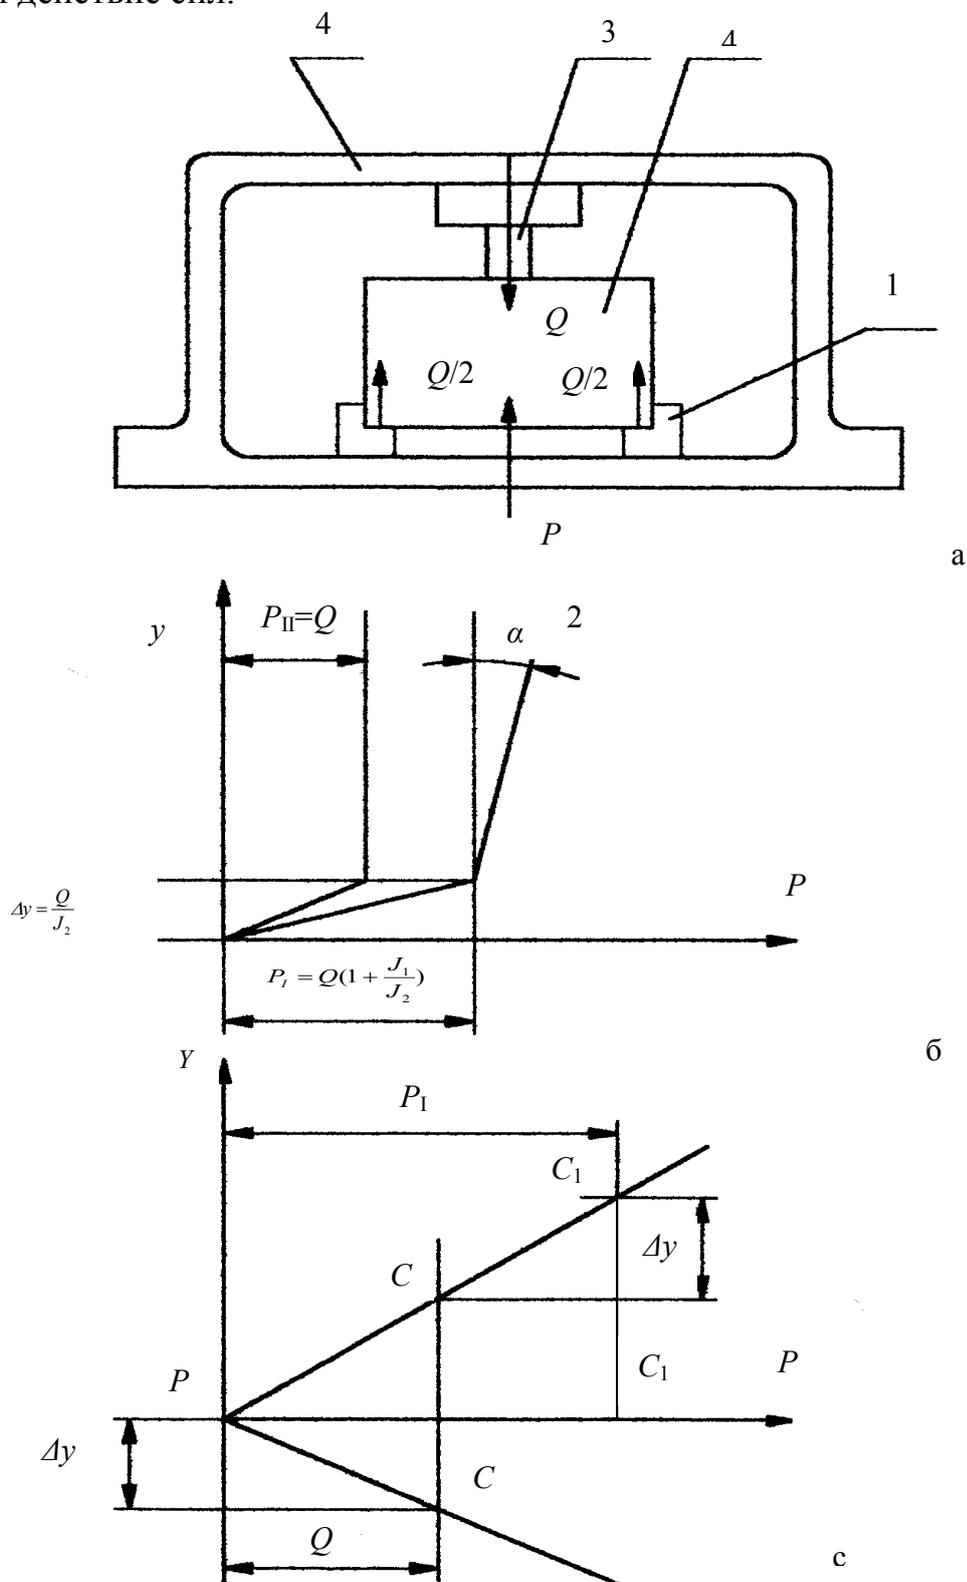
Действие сил на закрепленную в приспособлении заготовку
